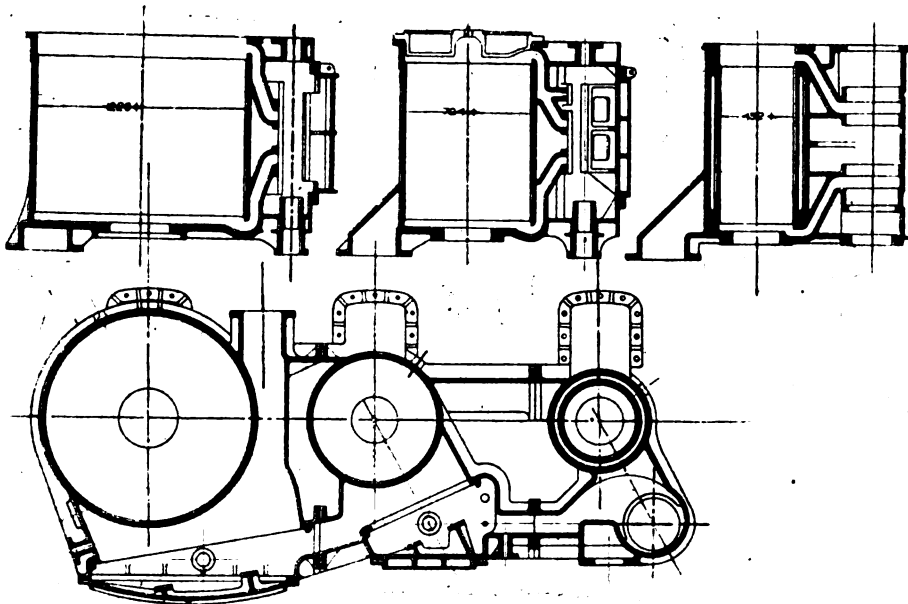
Dampfzylinder der Dreifachexpansionsmaschine für 500 PS
